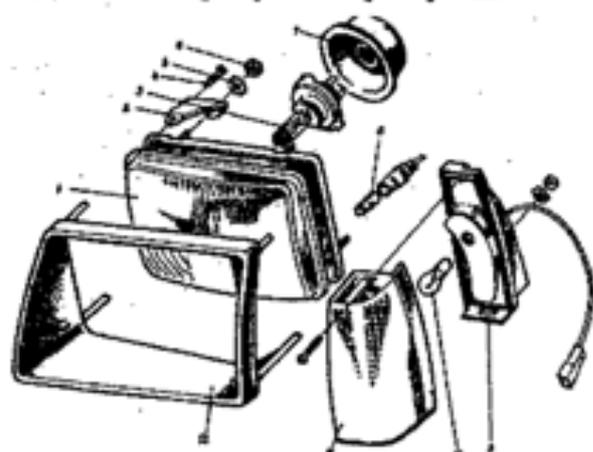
Фара: 1 - фара в сборе; 2 - кронштейн; 3 - лампа АКГ12-60 + 55 - 1(Н4); 4 - винт; 5 - шайба стопорная; 6 - гайка; 7 - колпак; 8 - лампа стояночного света А12-4-1; 9 - передний указатель поворота; 10 - лампа поворотов А12-21-3; 11 - рассеиватель; 12 - накладка фары.
